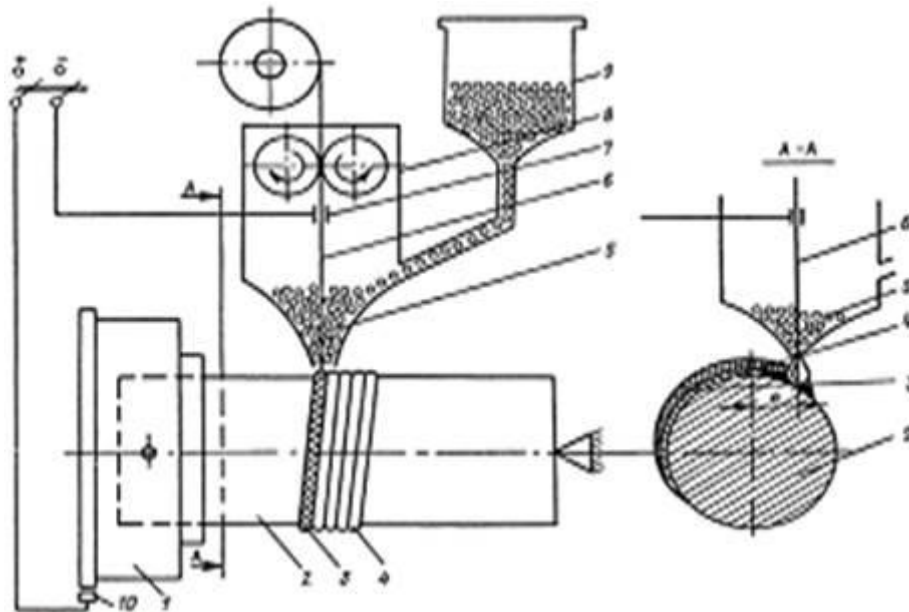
Схема установки для напівавтоматичного електродугового наплавлення деталей під шаром флюсу: 1 – патрон токарно-гвинторізного верстата; 2 – відновлювана деталь; 3 – шар шлаку; 4 – наплавлений метал; 5 – флюс; 6 – електродний дріт; 7 – контакт проводу від джерела струму з електродним дротом; 8 – наплавочний головка; 9 – бункер з флюсом; 10 – контакт проводу від джерела струму з мідною шиною патрона (деталлю); е – зміщення електрода щодо вертикальної осі деталі (ексцентриситет електрода)
